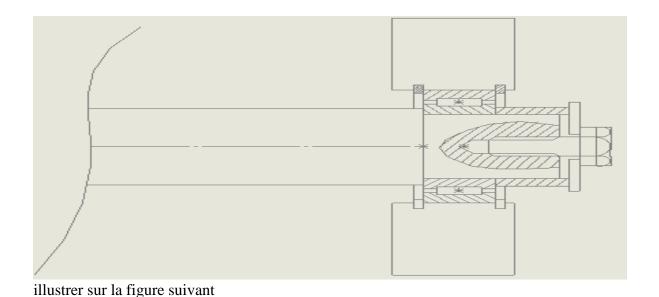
SCHEMA MONTAGE DU ROULEMENT ET DU GALET
